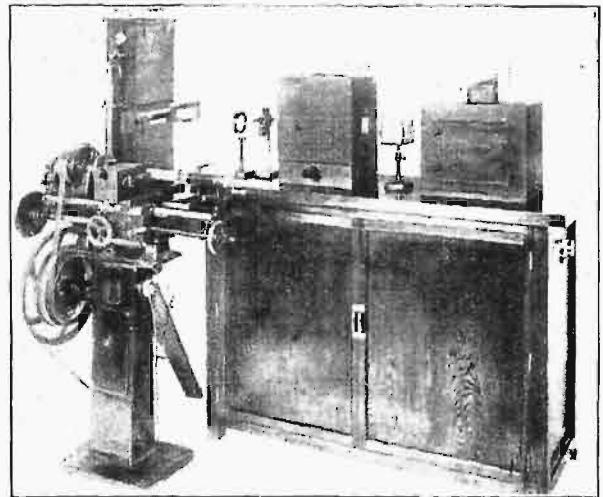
zapoznaje nas z wyglądem aparatu po zdjęciu pokryw. Rys. 4 przedstawia całość instalacji, składającej się z tokarki z napędem elektrycznym i aparatury rejestracyjnej.
